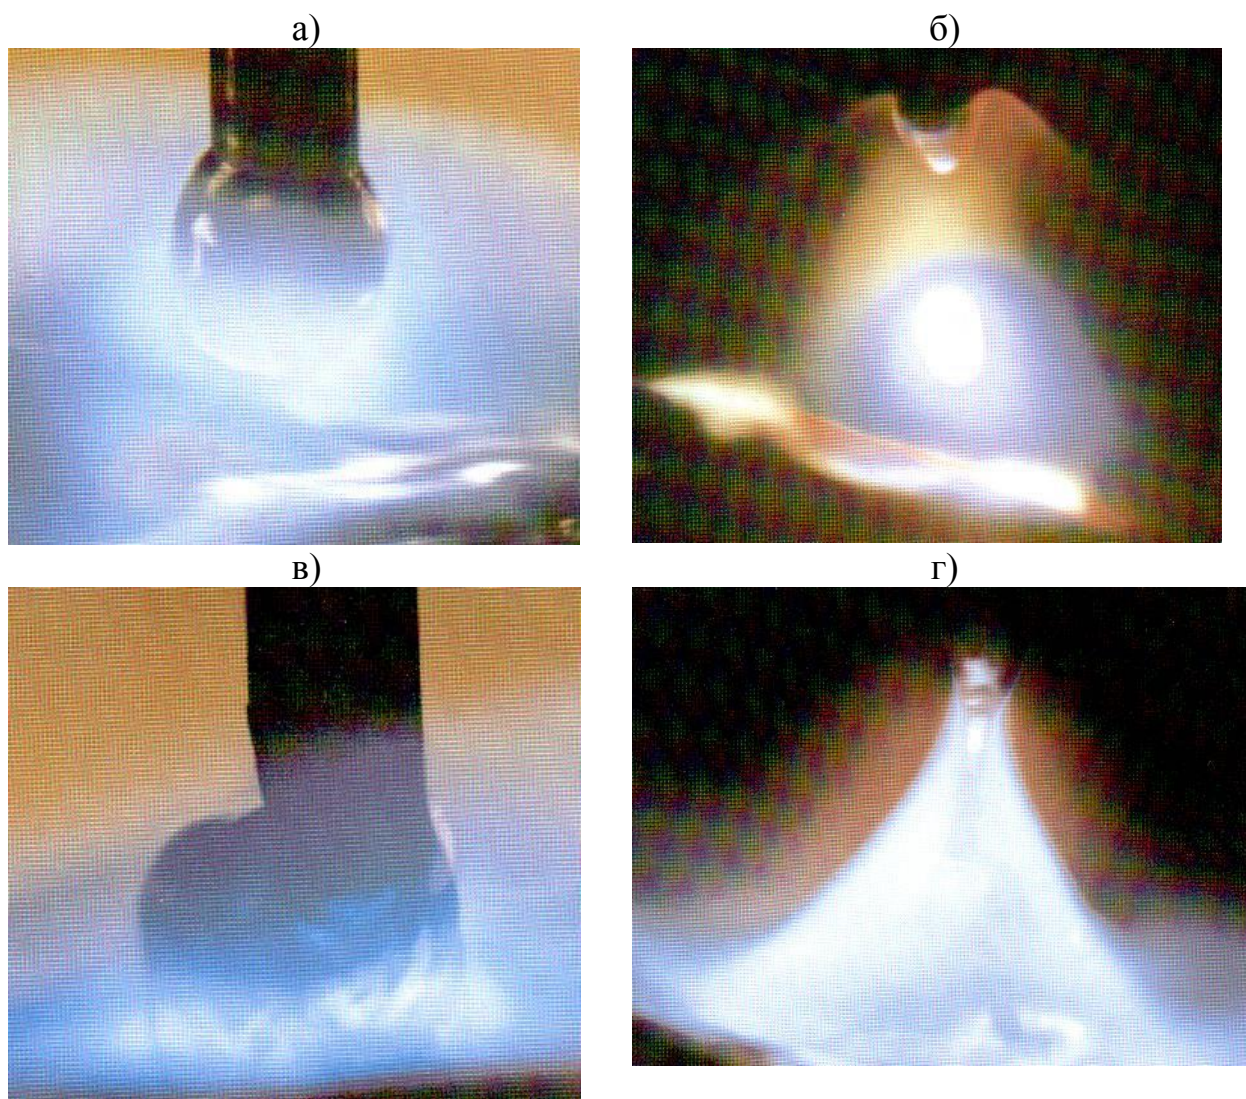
Горение дуги при различных типах переноса металла: сварка короткой дугой (а); сварка импульсной дугой (б); крупнокапельный перенос (в); сварка длинной дугой (г)
